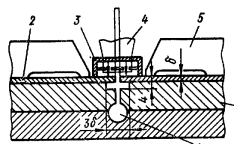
Схема защиты лицевой и обратной сторон соединения при механизированной аргодуговой сварке титана и его сплавов:
